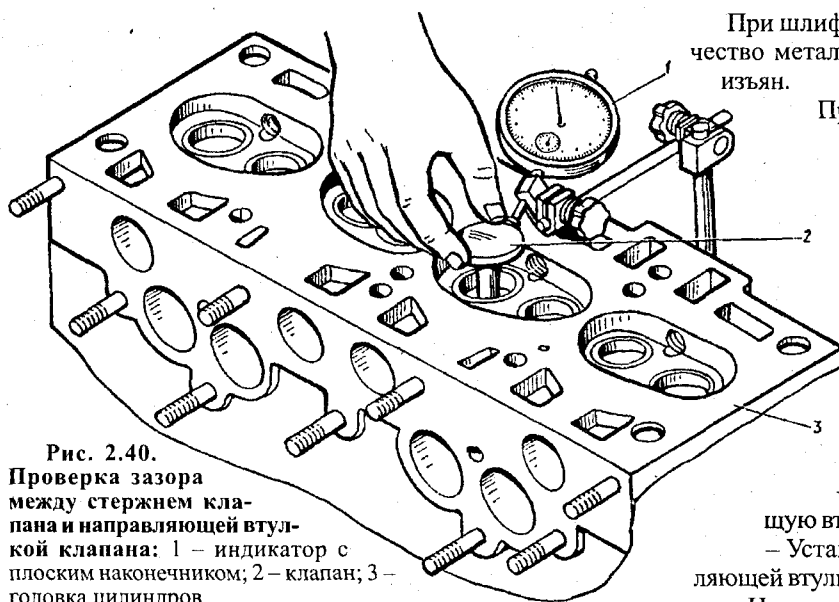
Проверка зазора между стержнем клапана и направляющей втулкой клапана: 1 – индикатор с плоским наконечником; 2 – клапан; 3 – головка цилиндров
